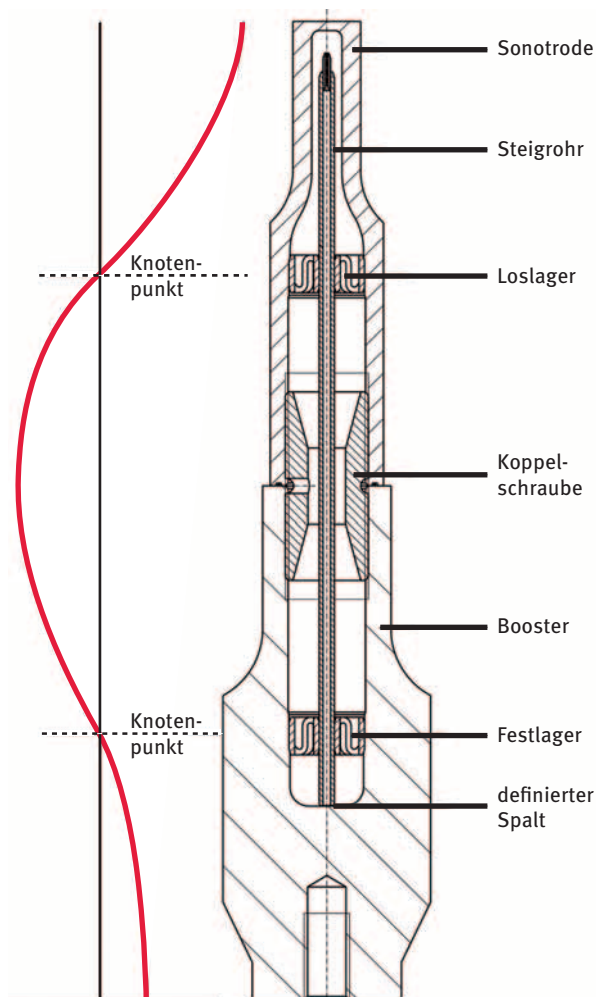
Zusammenschluss der Ultraschallpumpe und der Sonotrode zu einem gekühlten Ultraschallschweißwerkzeug
